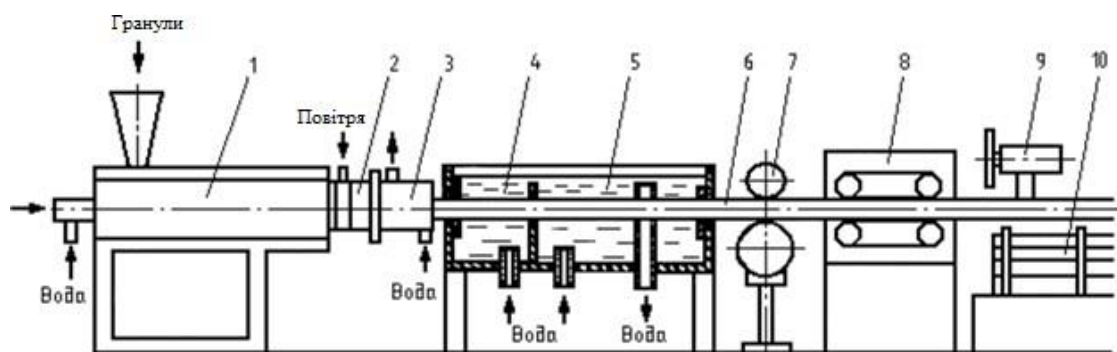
Схема агрегату для виробництва труб методом екструзії, де 1 - екструдер; 2 - формуюча головка; 3 - калібруюча насадка; 4, 5 - перша і друга зони охолодження; 6 - трубочастий профіль; 7 - вимірювально-маркіруючий пристрій; 8 - тягнучий пристрій; 9 - відрізаючий пристрій; 10 - приймальний стіл (штабелювальний пристрій)
